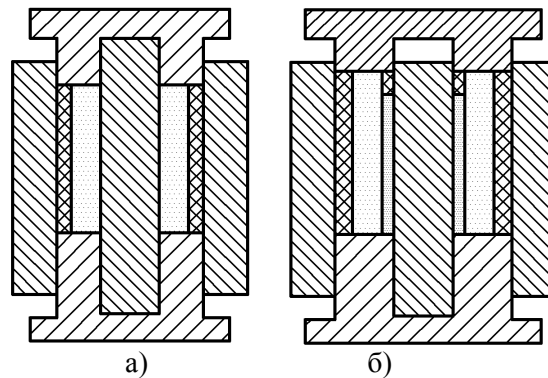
Схема прес-форми квазіізостатичного методу: а) – пресування шару-основи; б) – пресування другого шару
